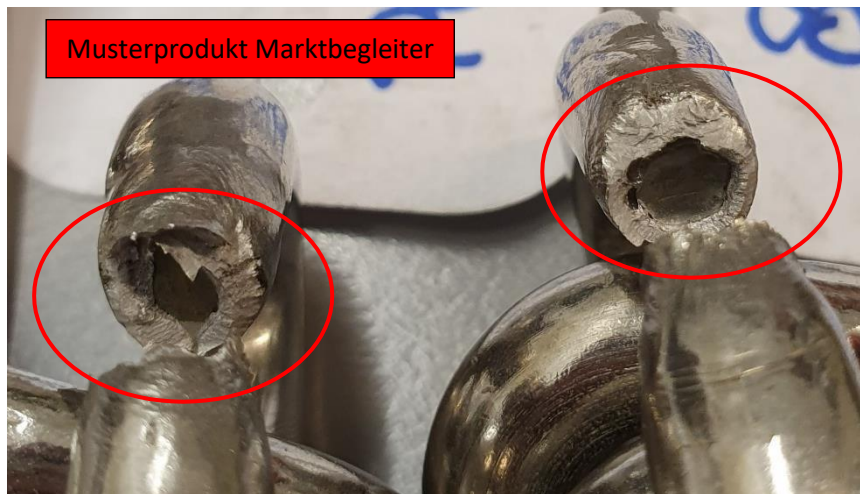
6x18,5 mm Schweißnahtbrüche beim Zugversuch
